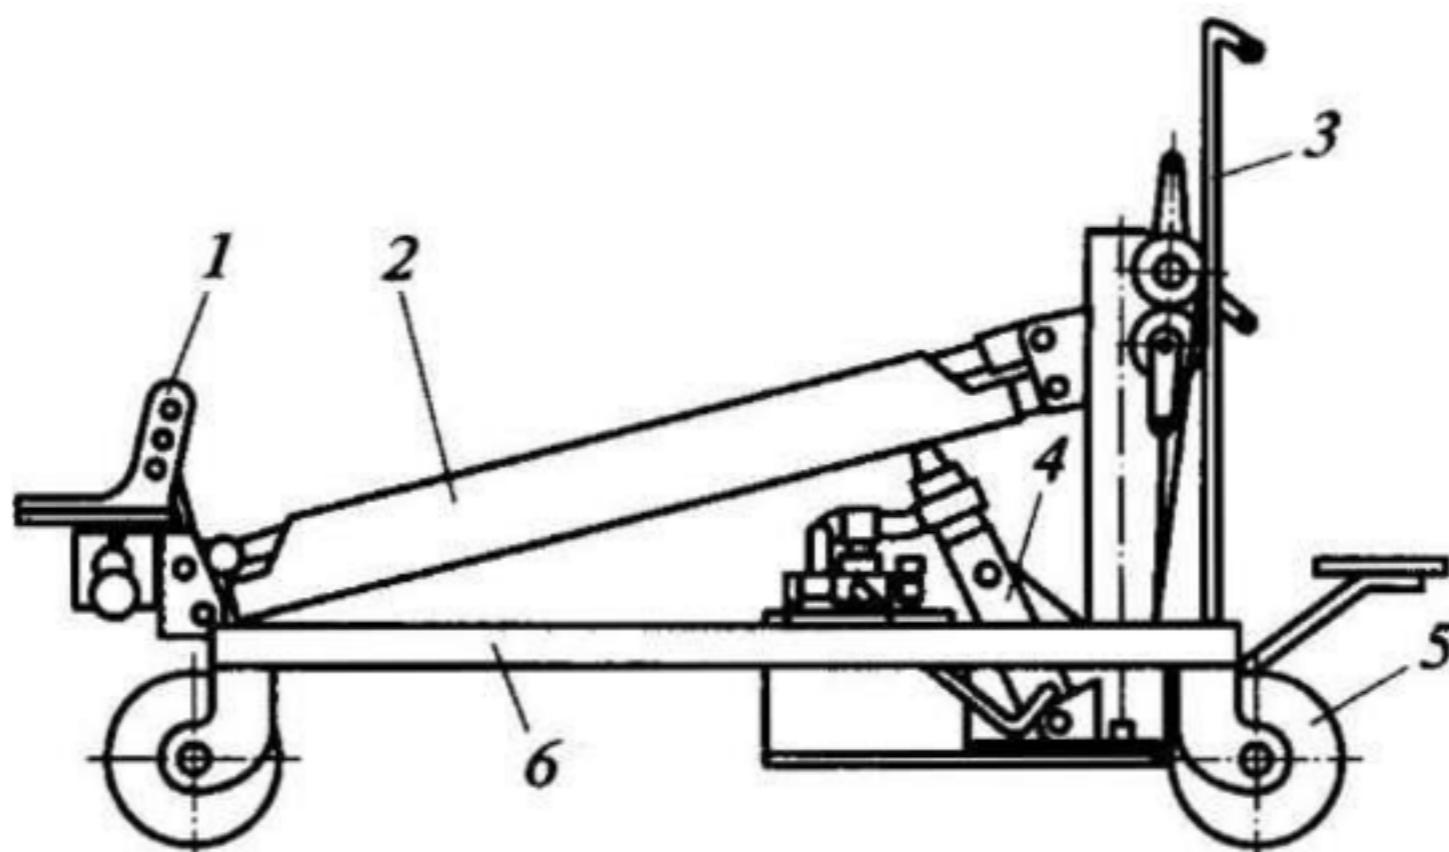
Тележка для снятия и постановки рессор: 1 — подхват для рессор; 2 — стрела; 3 — рукоятка; 4 — гидроцилиндр; 5 — колесо; 6 — продольная балка
